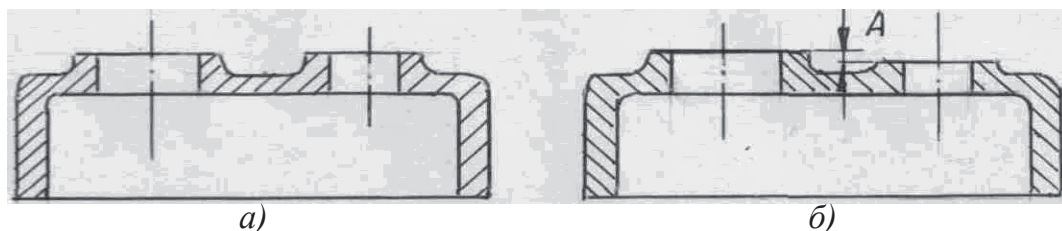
Схемы расположения наружных обрабатываемых поверхностей у деталей корпусного типа: *а* – технологичное; *б* – нетехнологичное
